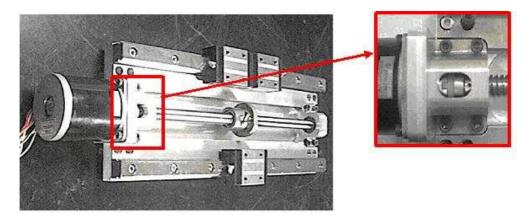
Posicionador para o eixo Y com motor de passo e acoplamento flexível em desataque.
